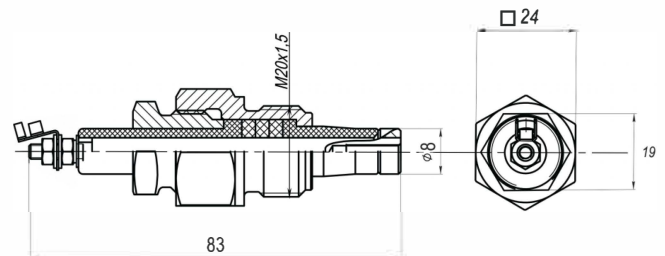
габаритные и установочные размеры датчика КДУ-1
